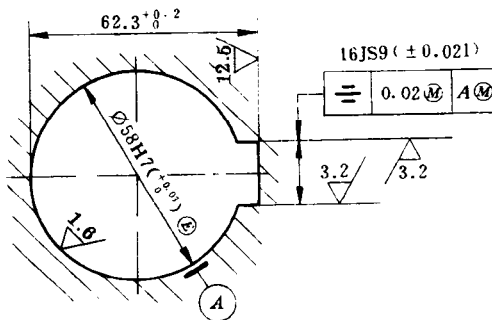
轮毂键槽尺寸和公差标注示例
